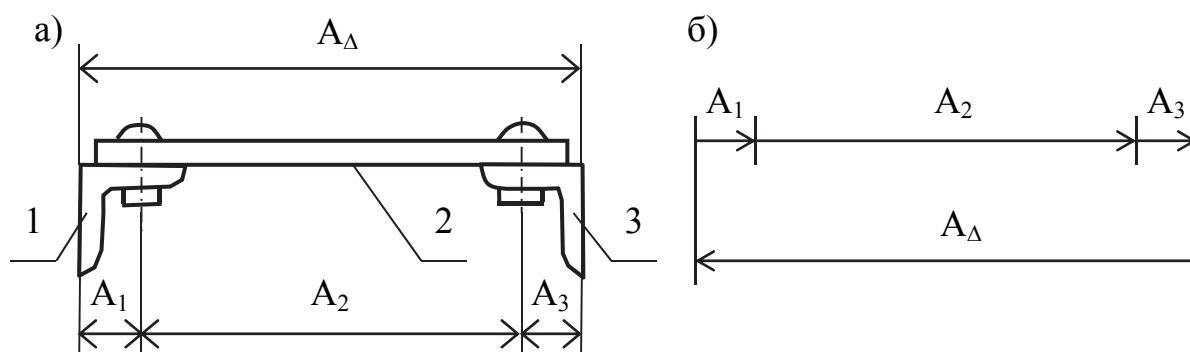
Эскиз узла (а) и схема сборочной цепи (б):
